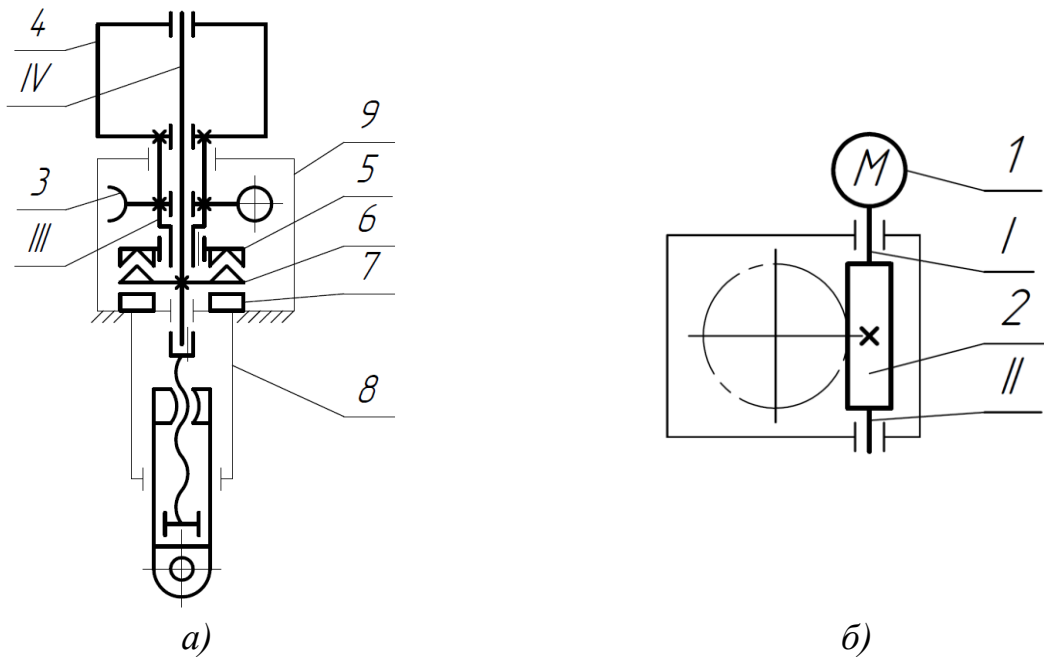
Кинематическая схема предложенного устройства в составе исполнительного механизма: а) — главный вид, б) — разрез по червячному колесу 3.
